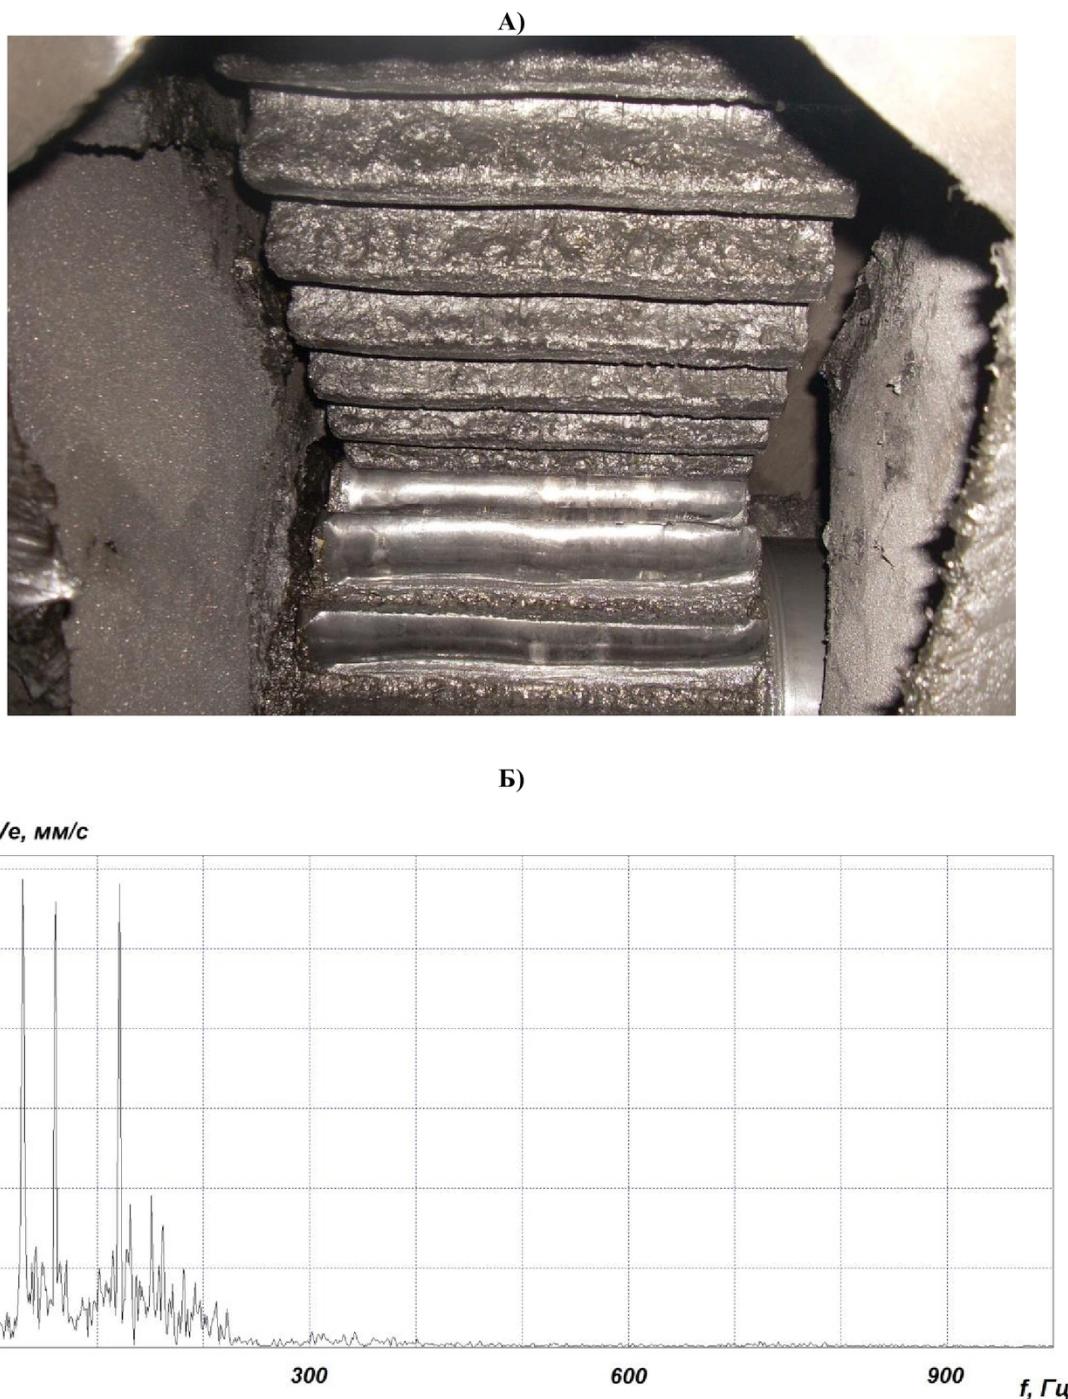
Абразивный износ зубчатых зацеплений открытой зубчатой передачи, недопустимый уровень расценцовки редуктора с открытой передачей подъемной лебедки экскаватора ЭКГ-5А (A – общий вид, Б – спектр по параметру виброускорения, записанный на подшипниковой опоре лебедки).
